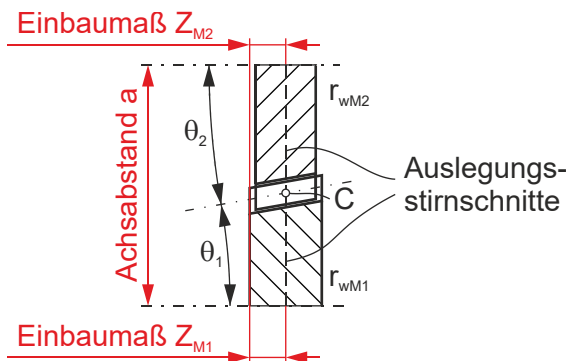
Einbaugeometrie bei paralleler Achslage
